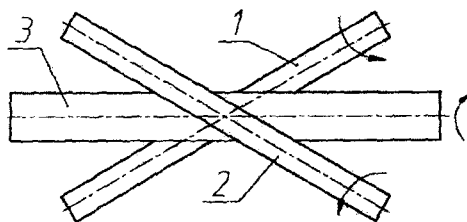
Поперечно-винтовая прокатка: 1, 2 – валки; 3 – заготовка
